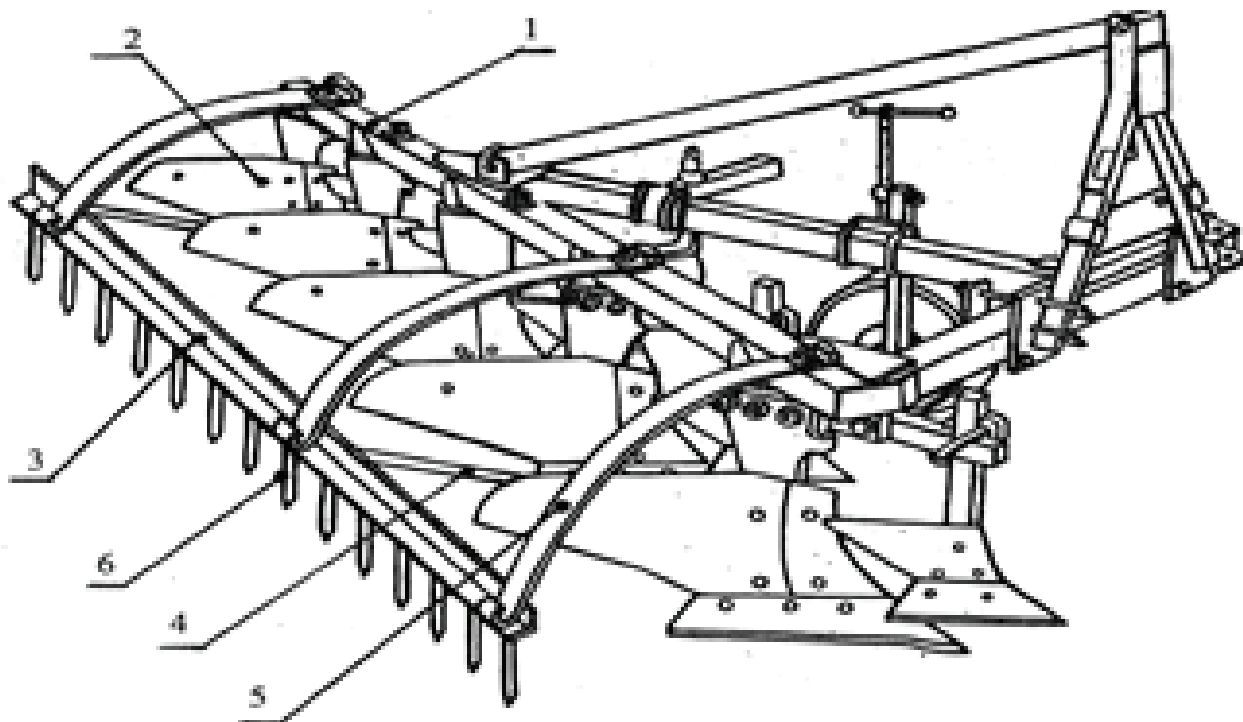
Комбинированный почвообрабатывающий агрегат:
